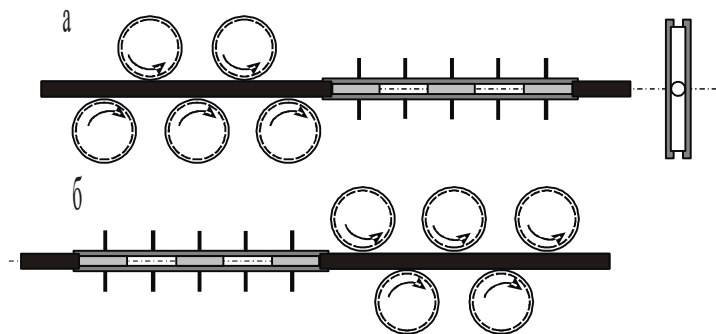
Схема правильного пристрою багагороликового верстата: а - вид збоку; б - вид зверху
